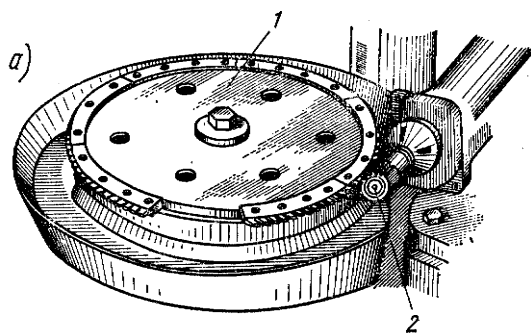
Круговое протягивание зубьев конического зубчатого колеса: 1- круговая протяжка; 2- нарезаемое колесо.
